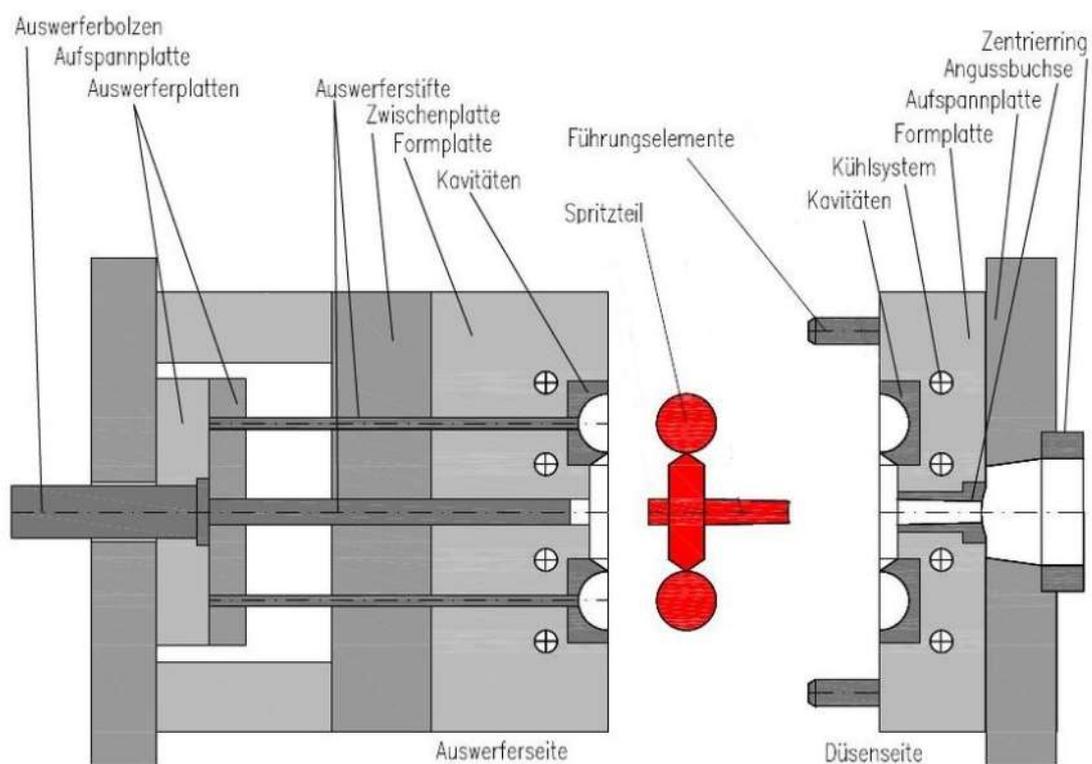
Der Aufbau eines Spritzgießwerkzeuges [38]
